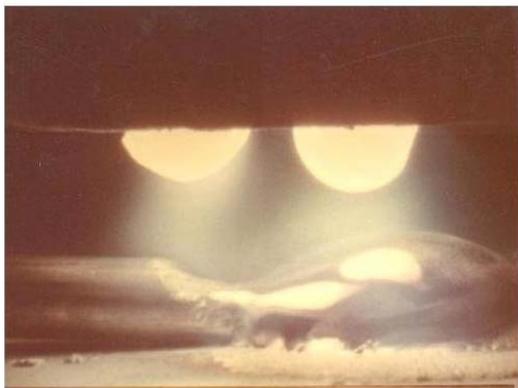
Процесс наплавки поверхности изделия из алюминиевого сплава трехфазной дугой
